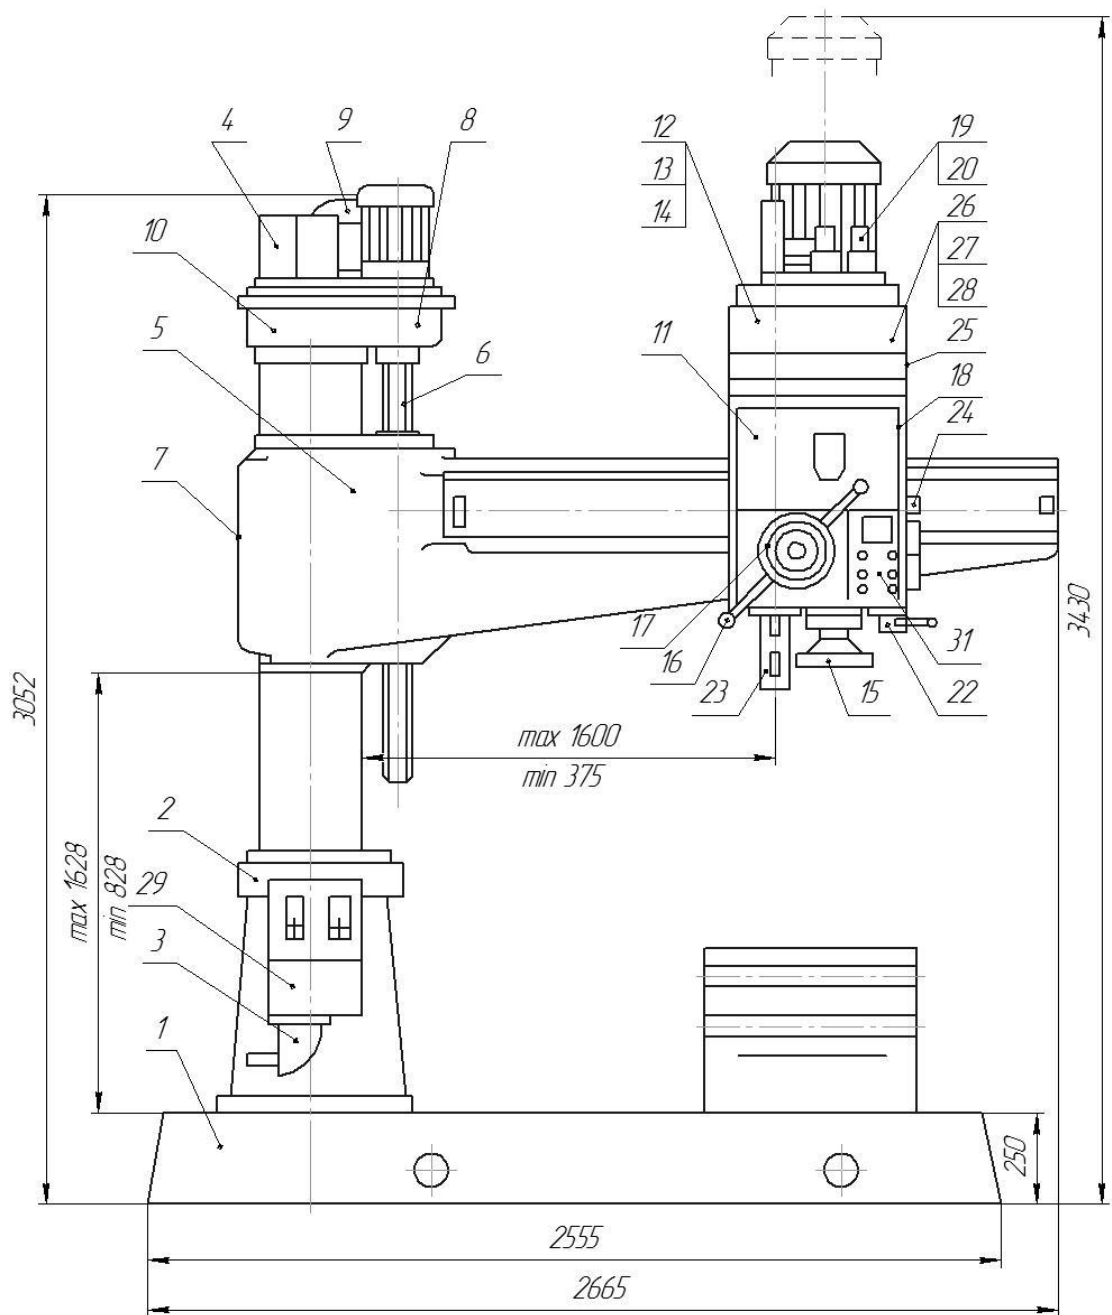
Загальний вид радіально-свердлильного верстата 2М55
